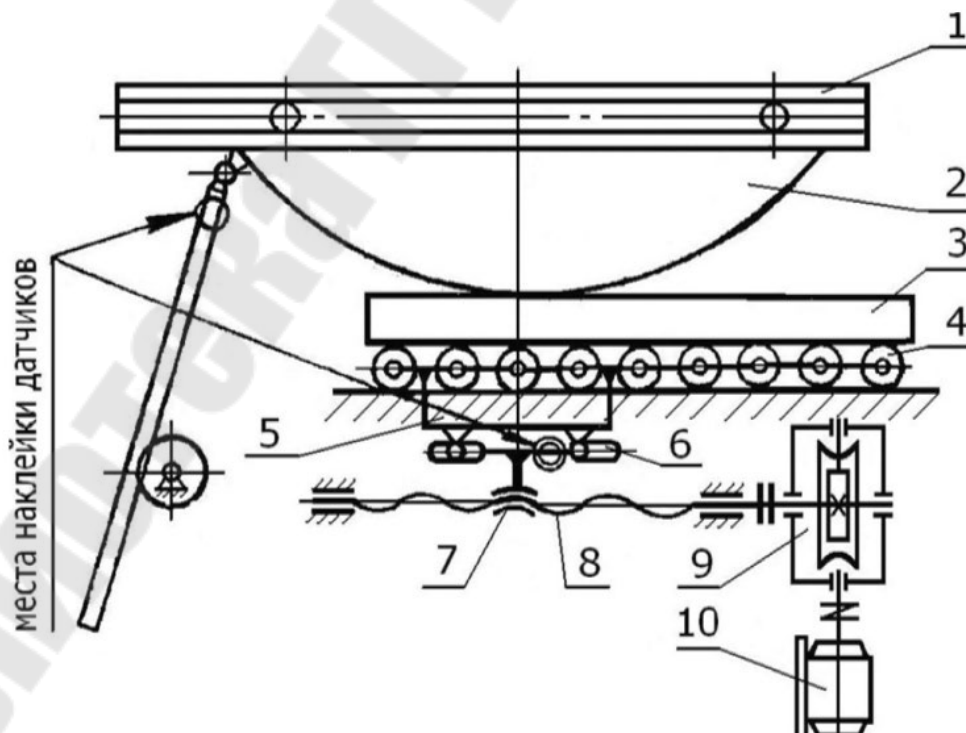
Кинематическая схема механизма выката корпуса электросталеплавильной печи
